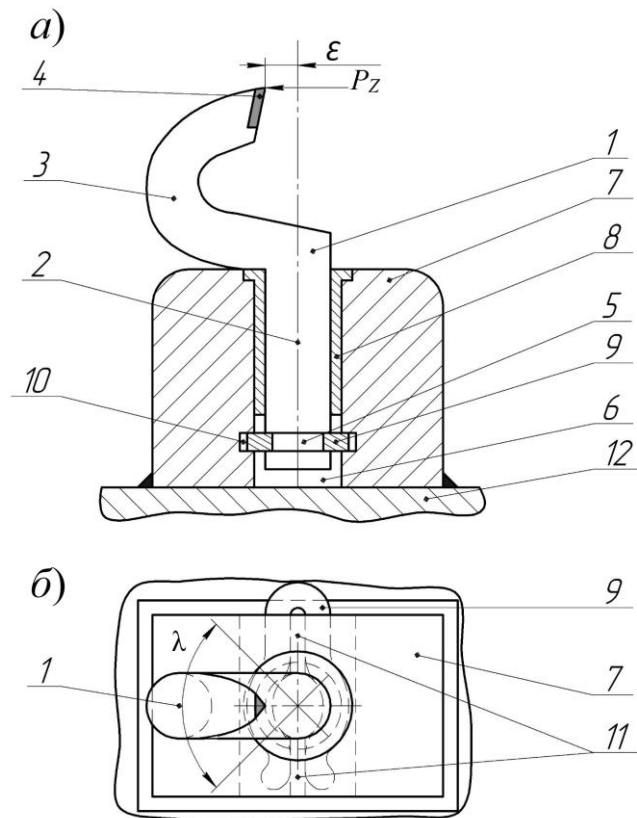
Самоустанавливающийся резец, размещенный в резцедержателе на исполнительном органе горного комбайна: *а* – вид сбоку; *б* – вид сверху
